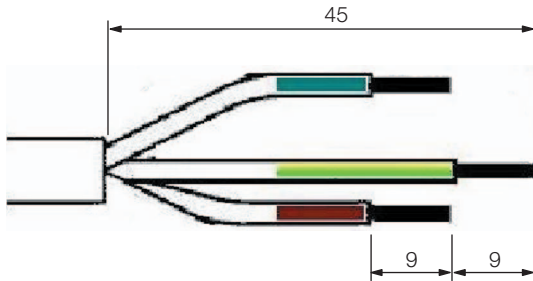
Maße zum Entfernen der Gummiummantelung und der Isolierung
